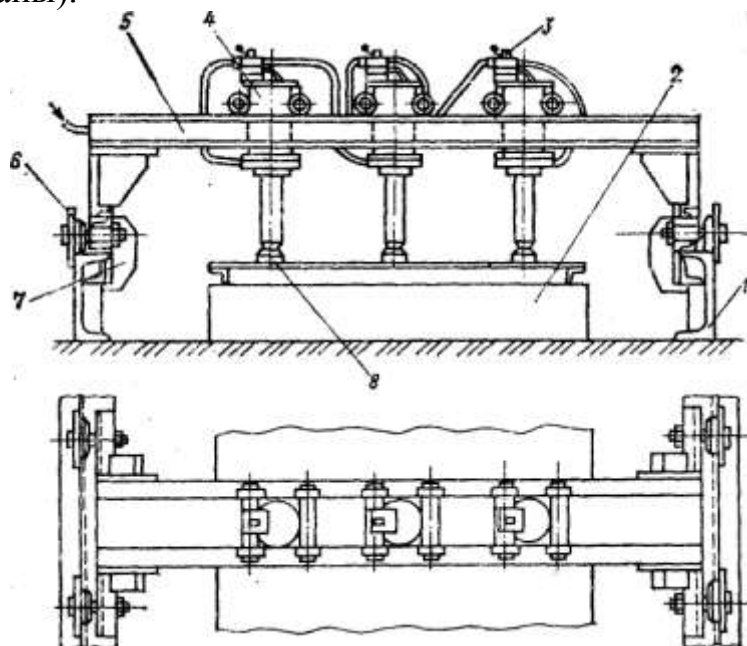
Стенд для сборки и сварки полотнищ
